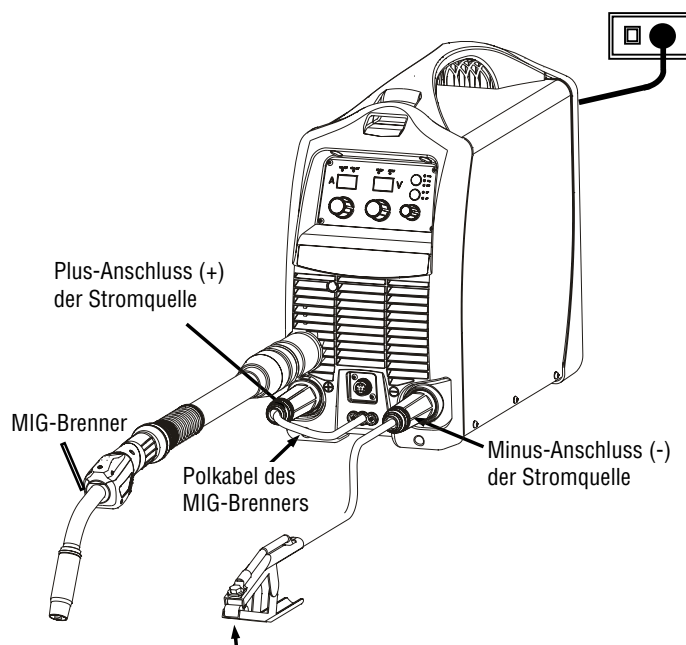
Konfiguration für MIG-Schweißen mit MIG-Schweißdraht ohne Schutzgas
